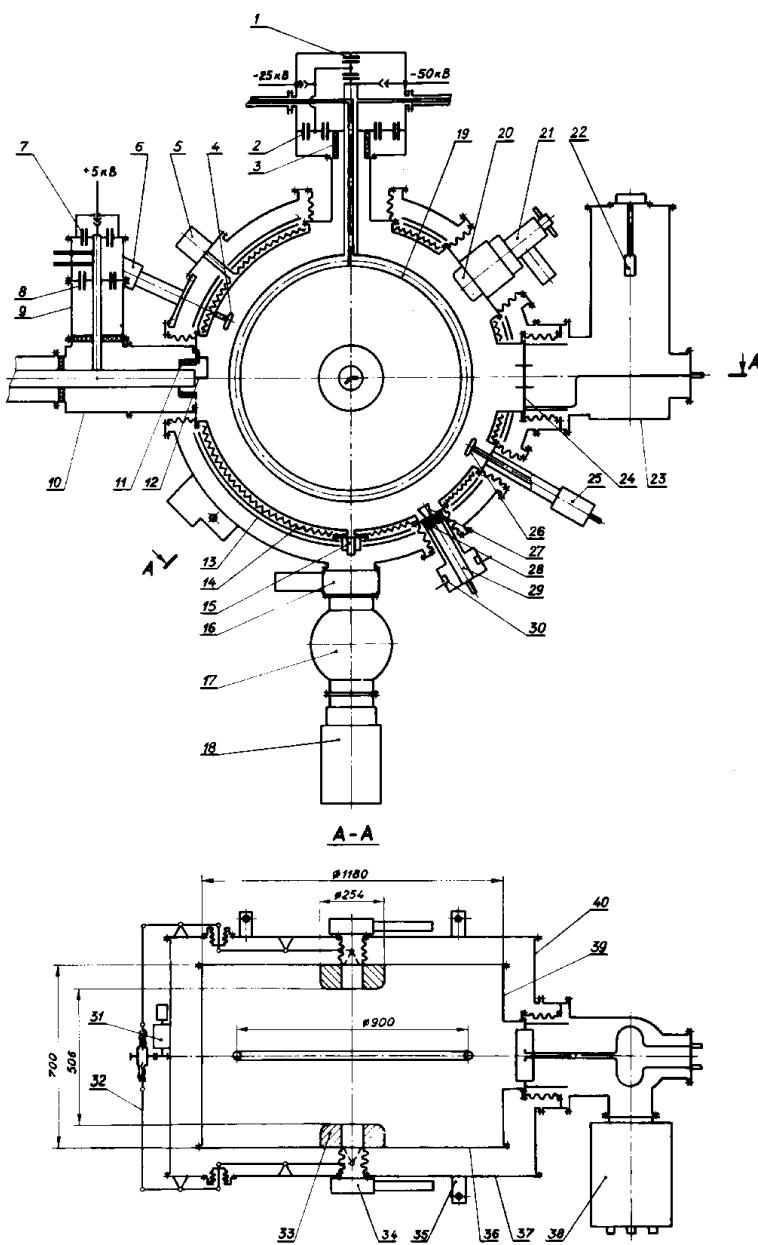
Схематический чертеж двухкамерного резонатора 181 МГц. 1, 2, 7, 8 – блокировочные конденсаторы; 3, 11, 28 – керамические изоляторы; 4, 20, 26 – элементы подстройки высших мод; 6, 21, 25 – приводы подстройки; 5 – вывод нагревателей и термопар; 9 – четвертьвольновый стакан; 10 – узел ввода мощности; 12 – петля связи; 13 – тепловые экраны; 14 – нагреватели; 15 – перепускной клапан; 16, 34 – вакуумные шиберы; 17 – азотная ловушка; 18, 38 – магниторазрядные насосы; 19 – противоразрядное кольцо; 22 – испаритель титана; 23 – сорбционный насос; 24 – электромагнитный экран; 27 – измерительная петля; 29 – отрезок коаксиальной линии; 30 – датчики напряжения; 31 – привод подстройки основной частоты; 32 – механизм подстройки; 33, 36, 39 – корпус резонатора; 37, 40 – вакуумный кожух; 35 – геодезические знаки.
